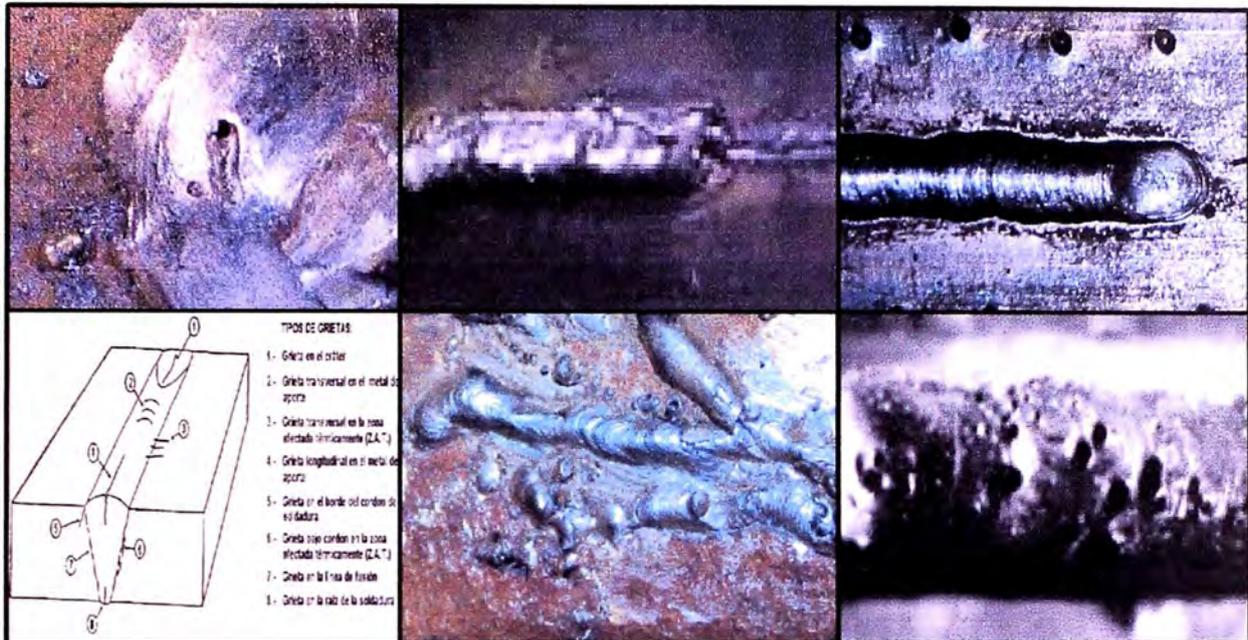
Defectos visuales de soldadura: Socavación, sobremonta, cráter, fisuras, inclusión de escoria y porosidad
